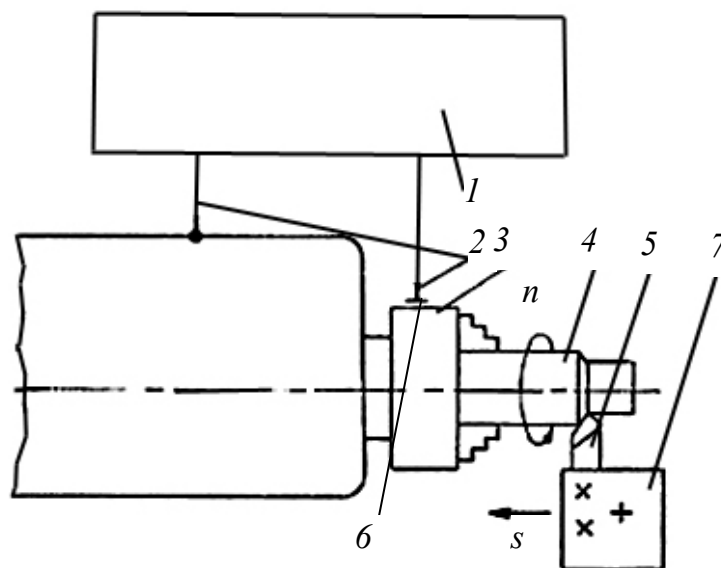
Схема прибора для измерения отжатий вращающихся деталей:
